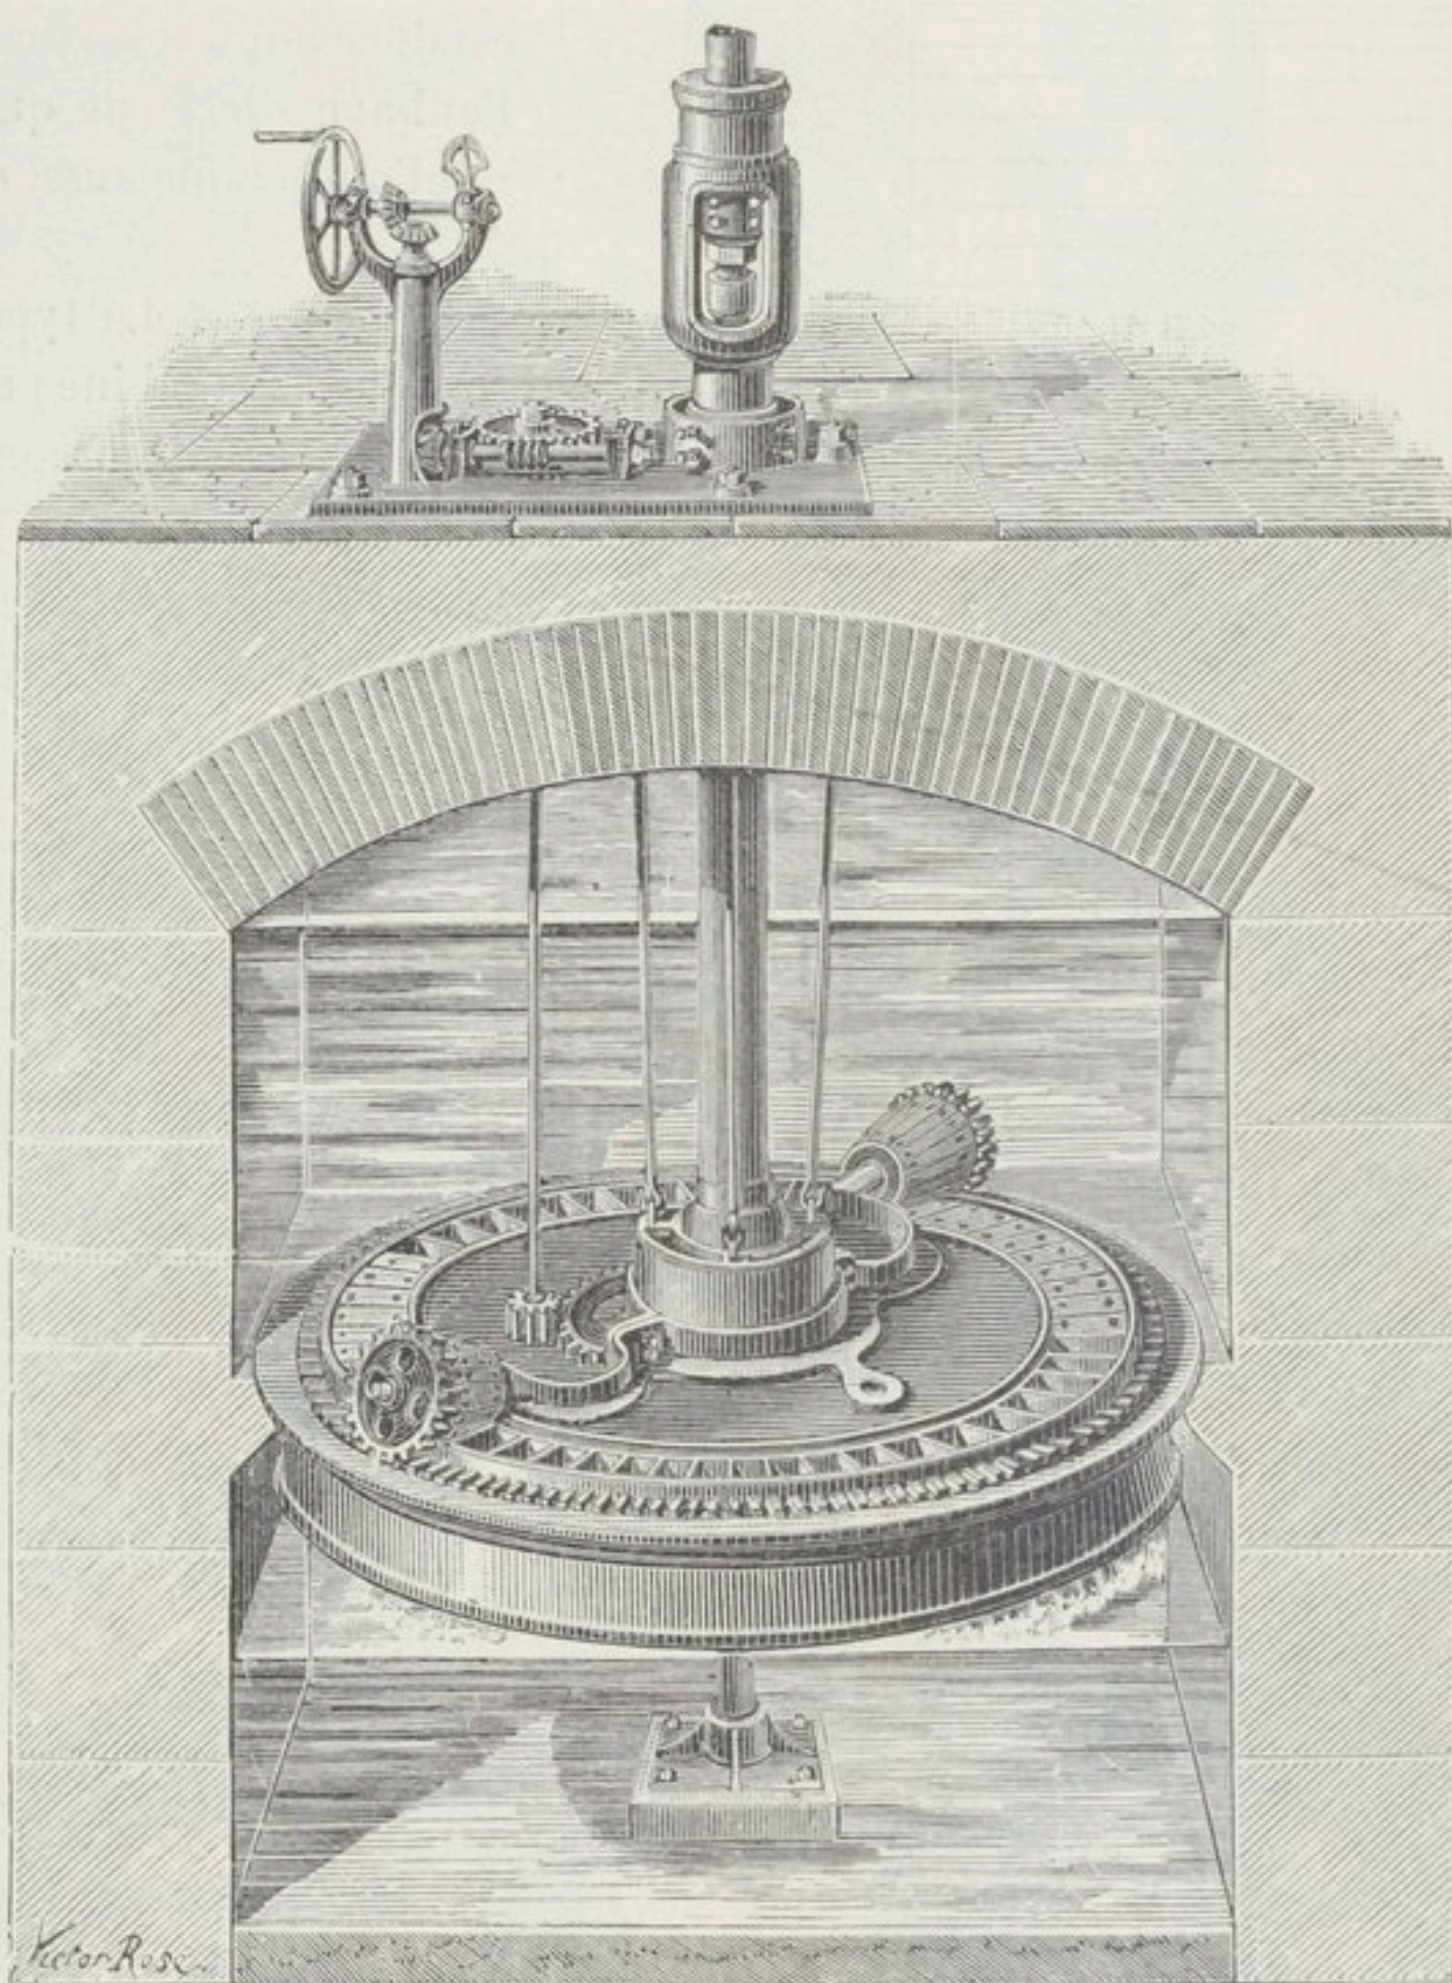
Turbine Fontaine. (Teisset, Chapron et Brault.)
